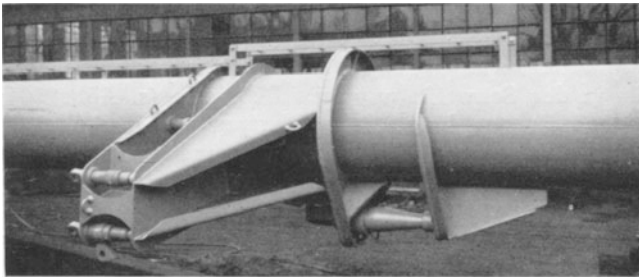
Geschweißter Schiffsstahlmast.
